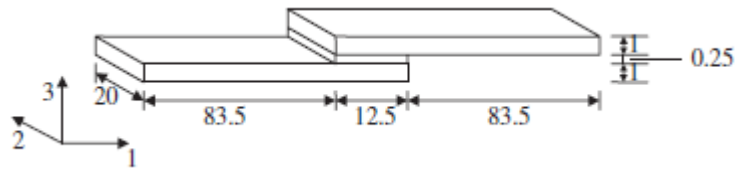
Geometria e dimensões da junta (de Moura et al. 2006).
